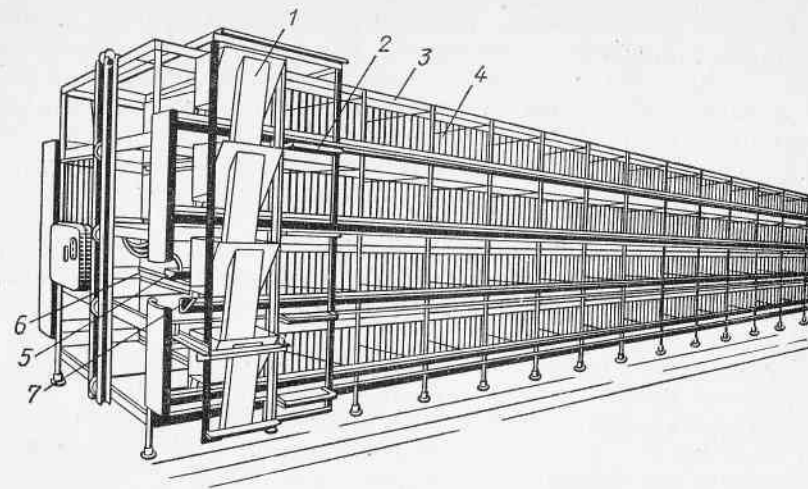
Клеточная батарея КБН-1 для кур-несушек: 1 — кормораздатчик; 2 — яйцесборочный механизм; 3 — каркас; 4 — клетка; 5 — поилка; 6 — скребок; 7 — кормушка.
